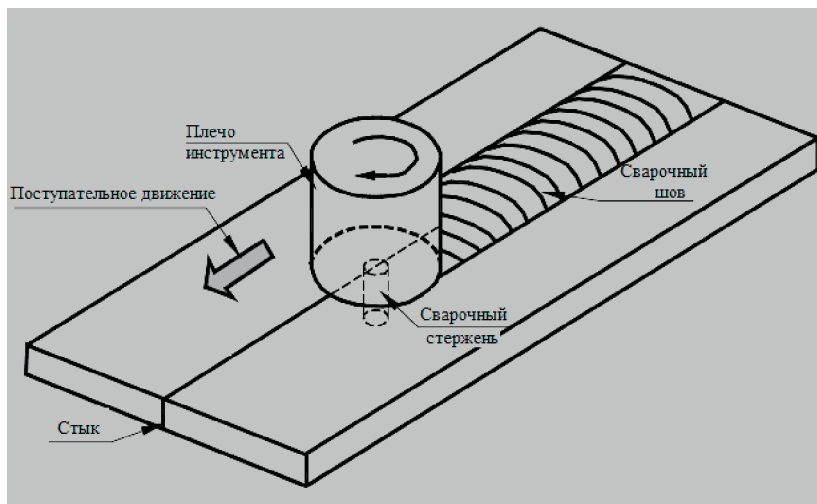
Схема процесса сварки трением с перемешиванием
